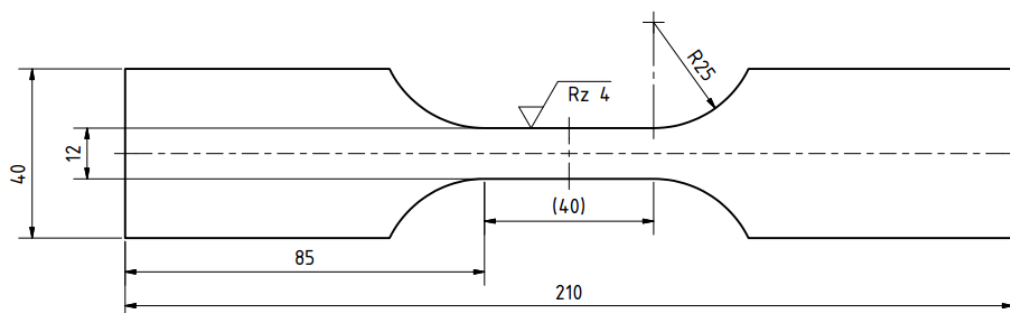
10 – Эскиз образца для проведения испытаний сварных соединений
